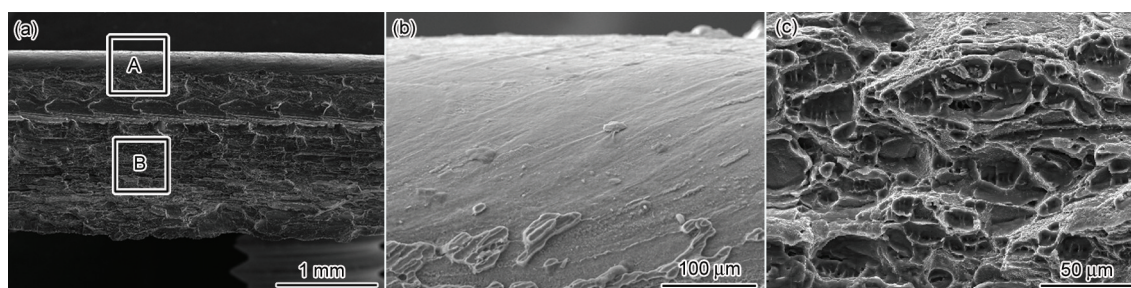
转速 600 r/min, 搅拌针长 3.0 mm 工艺条件下 2099-T83/2060-T8 Al-Li 合金 FSW 搭接接头剥离试样断口形貌
